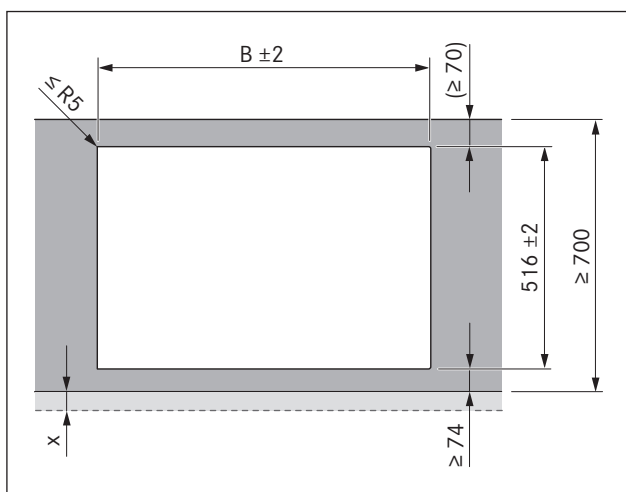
Rozmery drážky pre zapustenú montáž
